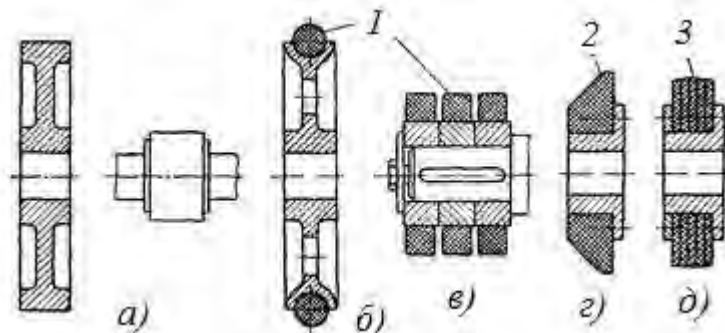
Конструкція котків фрикційних передач з металу(а), збірні насадної конструкції з неметалевими матеріалами(б-д):
